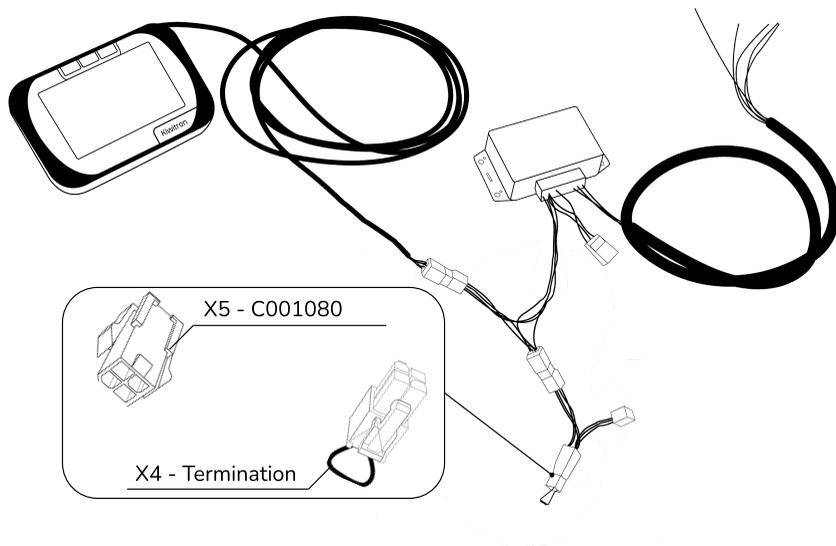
Collegamento terminazione X4 (chiusura CAN)
